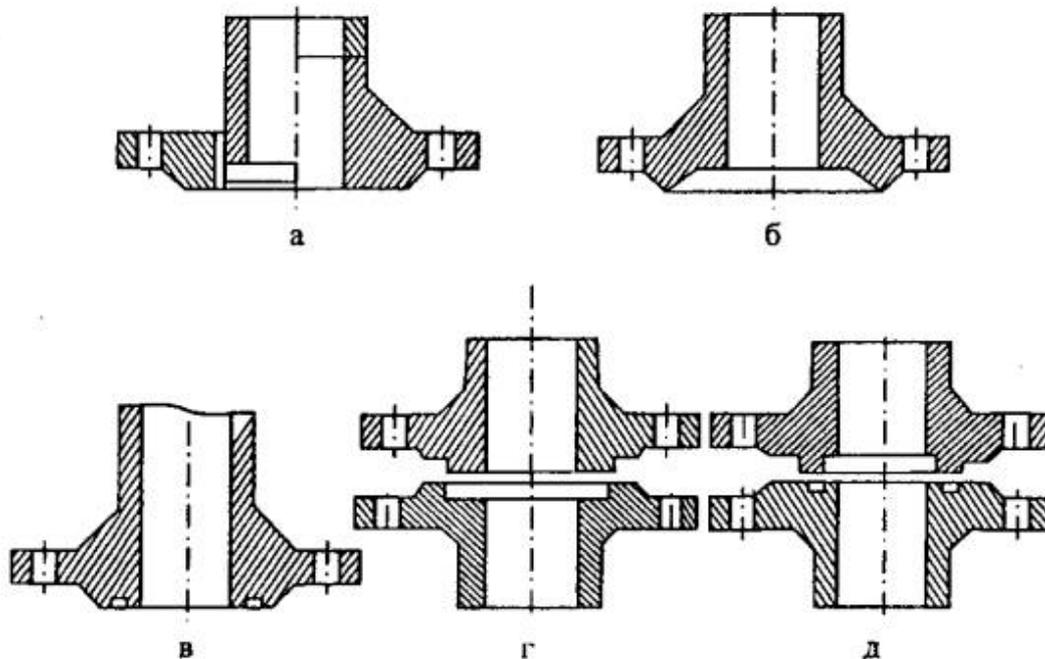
Уплотнительные поверхности фланцев арматуры и соединительных частей трубопроводов: а - гладкая; б - под линзовую прокладку; в - под кольцевую прокладку овального сечения; г - выступ - впадина; д - шип – паз.
